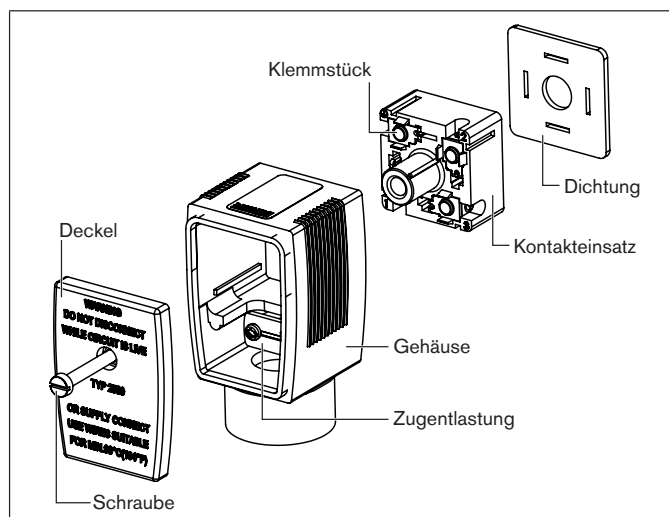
Explosionszeichnung Gerätesteckdose Typ 2509
